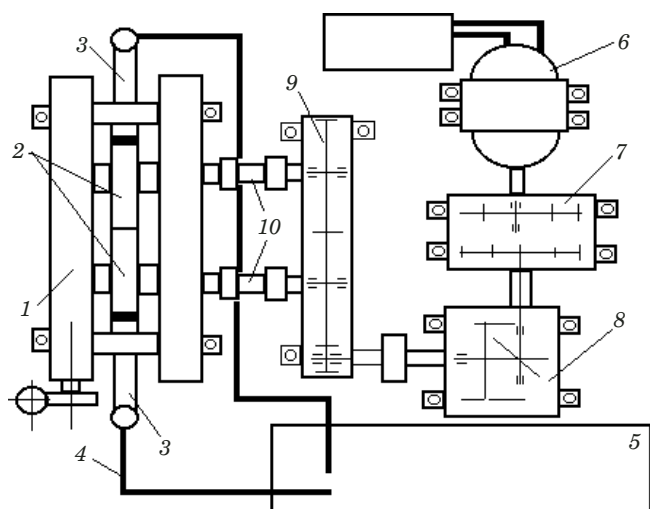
Схема УЭИС (вид сверху): 1 — рабочая клеть прокатного стана; 2 — валки-электроды; 3 — контактные устройства; 4 — токопроводы; 5 — энергоблок; 6 — электродвигатель постоянного тока; 7 — понижающий червячный редуктор; 8 — четырехступенчатая коробка передач; 9 — раздаточная шестеренная коробка; 10 — карданные штанги
